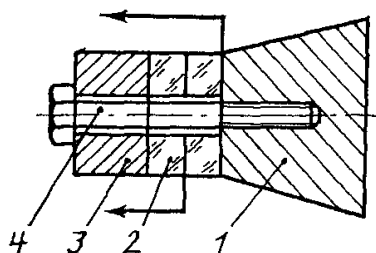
Составной пакетный преобразователь: 1 — коническая накладка; 2 — активный элемент; 3 — цилиндрическая накладка; 4 — стягивающий элемент
